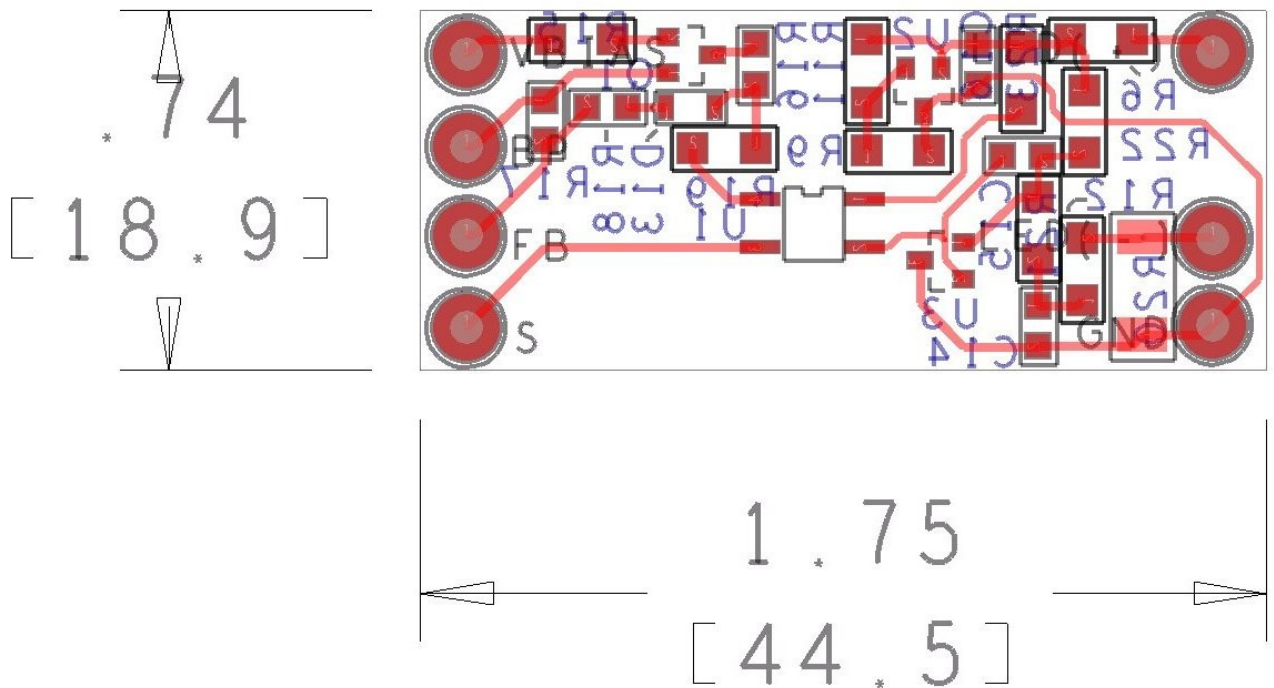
PCB 2 차측 정전류 레귤레이션 서브 보드 레이아웃(이 레이아웃과 일치하는 실제 회로도는 부록 A에 있음)
